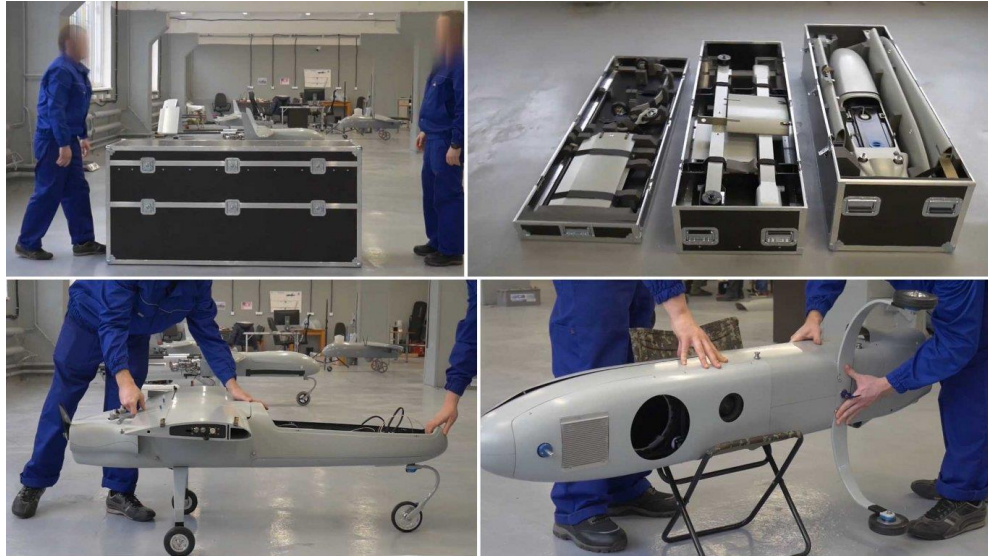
розпаковка та збірка деталей PD-2-VTOL
